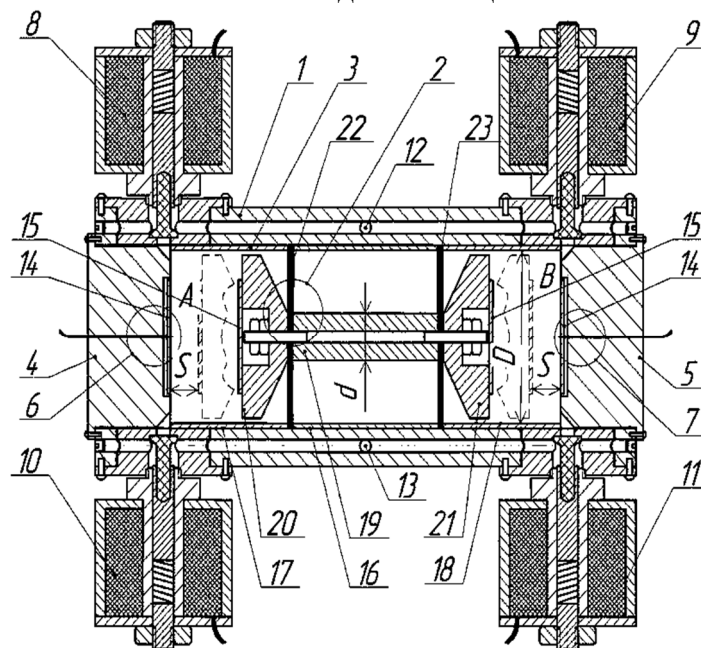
Схема расходомера топлива: 1 – корпус; 2 – поршень; 3 – измерительный цилиндр; 4 и 5 – крышки; 6 и 7 – ёмкостные датчики; 8, 9, 10 и 11 – электромагнитные клапаны; 12 – подводящий штуцер; 13 – отводящий штуцер; 14 и 15 – металлические обкладки конденсатора; 16 – центральный элемент измерительного цилиндра; 17 и 18 – крайние элементы измерительного цилиндра; 19 – центральный элемент поршня; 20 и 21 – крайние элементы поршня; 22 и 23 – мембраны
